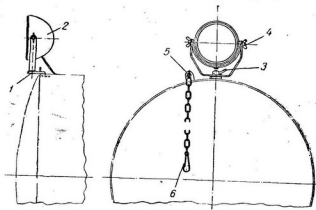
Установка фары и подвеска цепи заборного шланга АСМ-12: 1 — кронштейн; 2 — фара; 3 — гайка; 4 — барашки; 5 — ушко; 6 — цепь с карабином.
